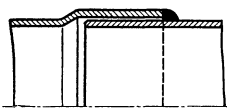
Schweißverbindung für Gasleitungen.
